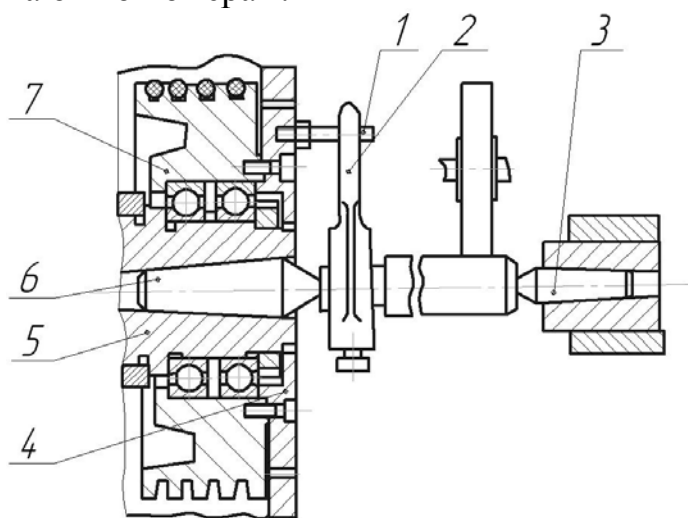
Схема установки заготовки в центрах: 1 — поводковый палец; 2 — хомутик (поводок); 3 — задний упорный центр; 4 — поводковая планшайба; 5 — шпиндель передней бабки станка; 6 — передний упорный центр; 7 — шкив
